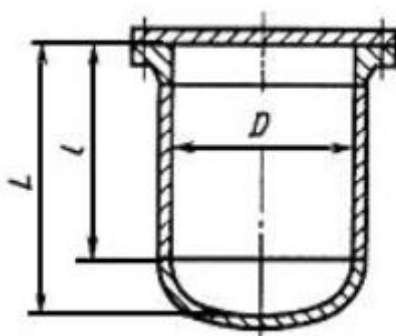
Корпус реактора с вертикальным эллипсоидным днищем и плоской крышкой (ВЭП 2)
